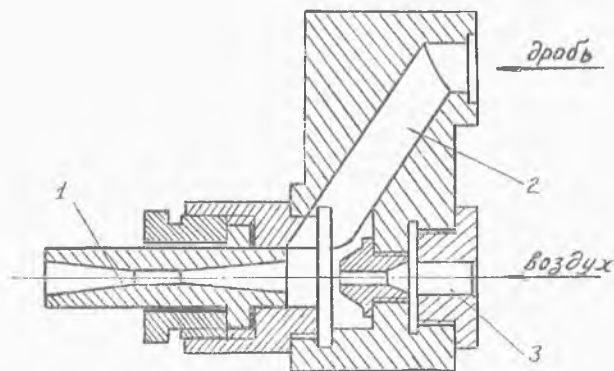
Рабочая форсунка пневмодробеструйной установки конструкции НИАТ: 1 — рабочее сопло; 2 — канал подачи дробы; 3 — воздушный канал
